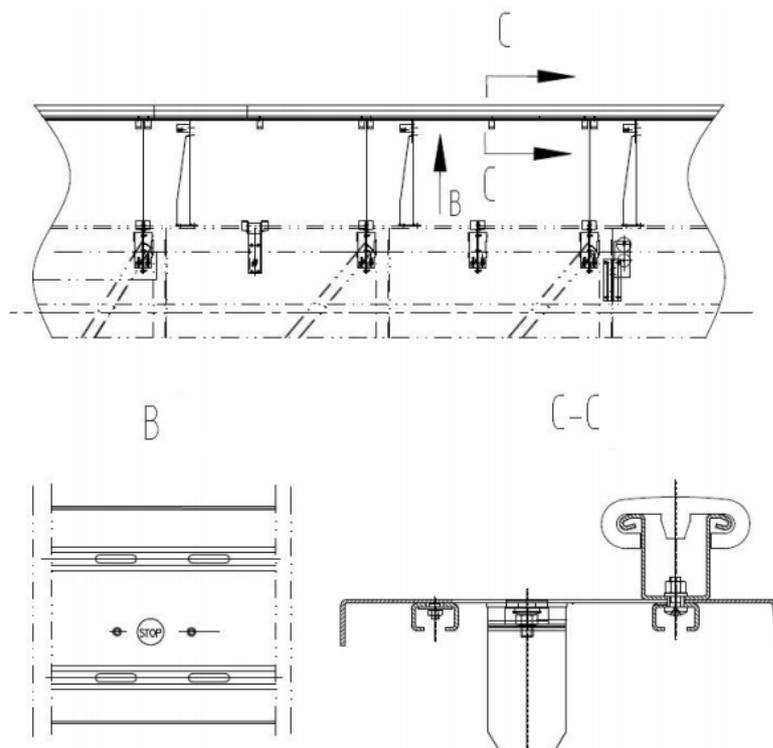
Выключатель аварийной остановки для металлической балюстрады.
